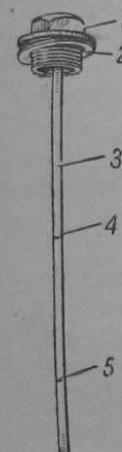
Щуп для проверки уровня масла в двигателе М-72:
